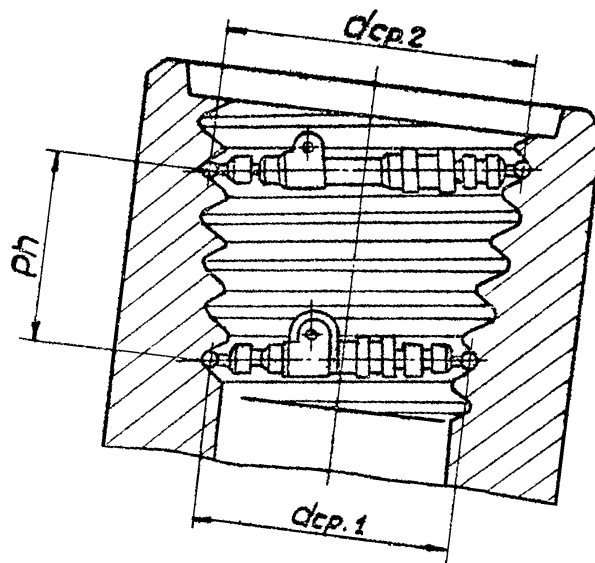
Рис. II. Проверка конусности внутренней резьбы накладным прибором типа MBK.
